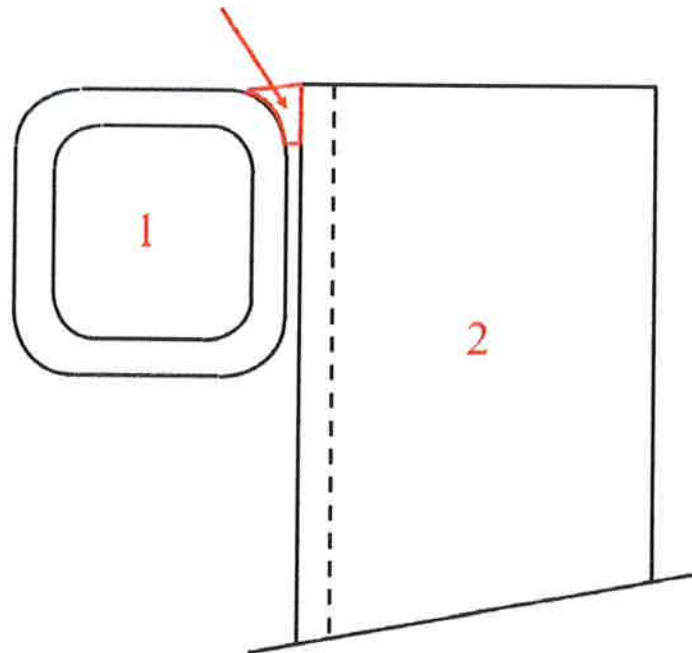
Vue de plan des 2 pièces, la flèche rouge pointe la soudure en demi-V à rebord tombé à réaliser (la région rouge illustre une soudure conforme à la norme CSA)
